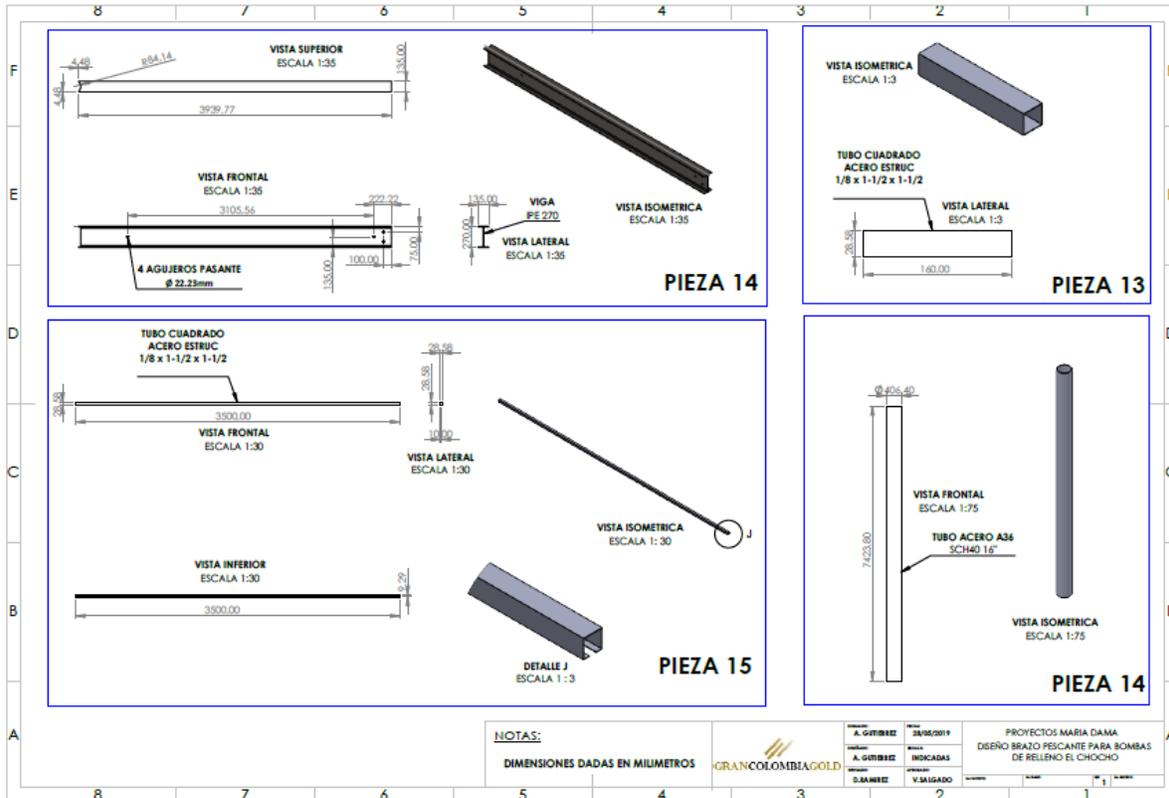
Plano #3 de piezas brazo pescante (Autoría Propia)
